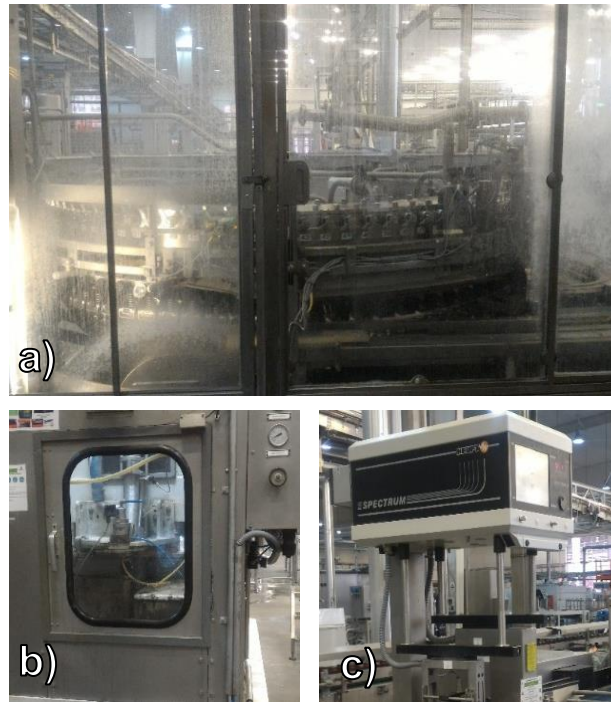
Enchedora, cravadora e inspetor de nível 1
